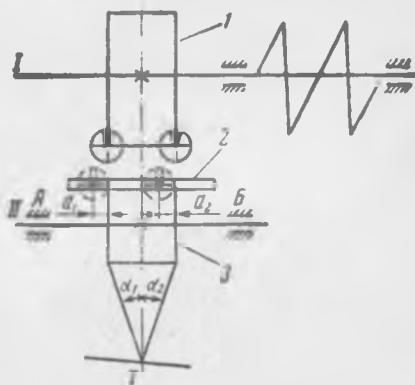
Схема проверки установки зубчатых колес с помощью теодолита:
